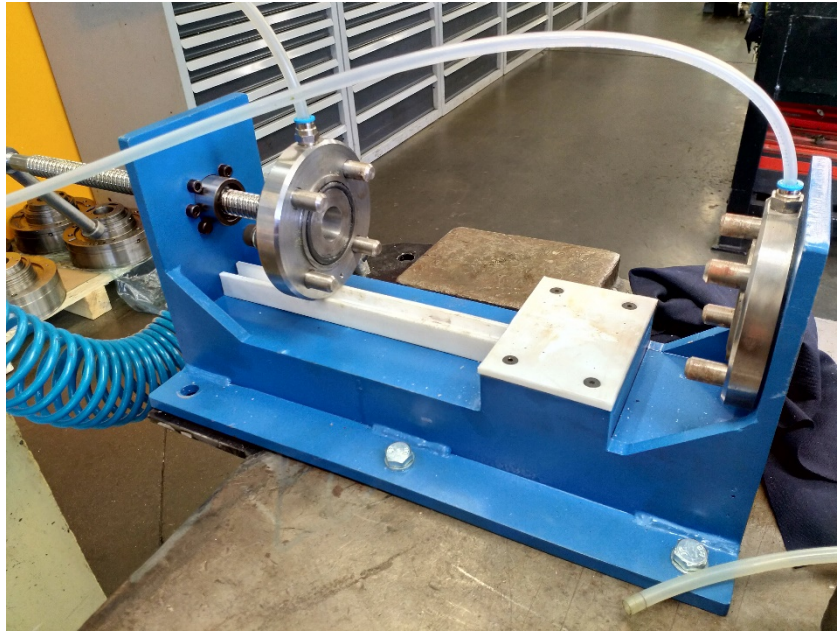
Equipamento de teste já fabricado – vista nº1.
